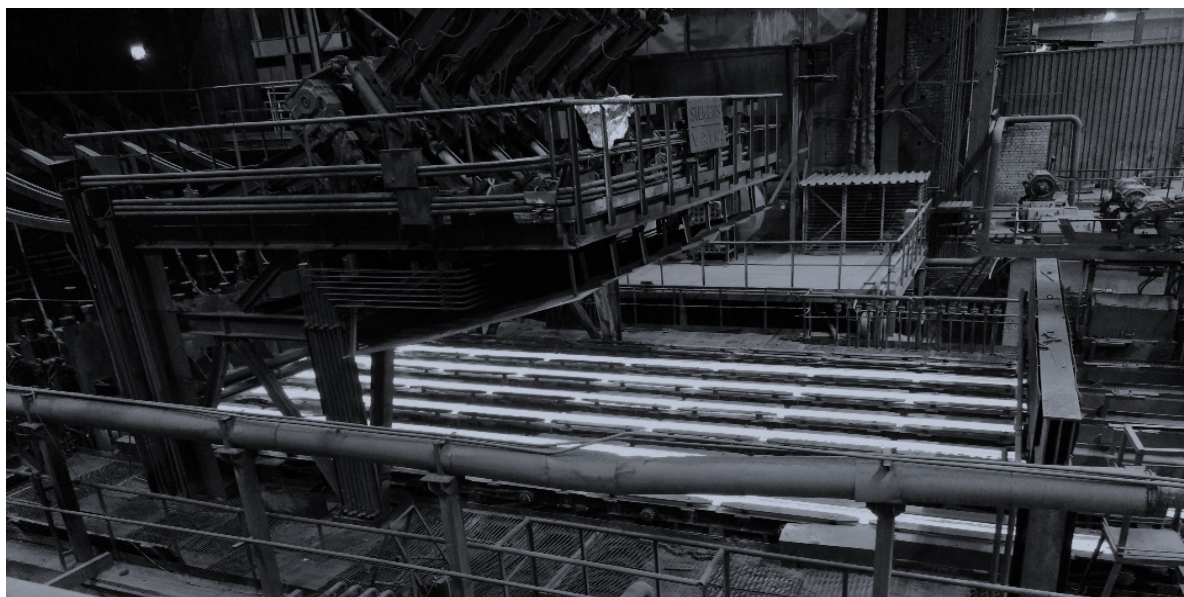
Загальний вигляд МБЛЗ під час розливної сталі
